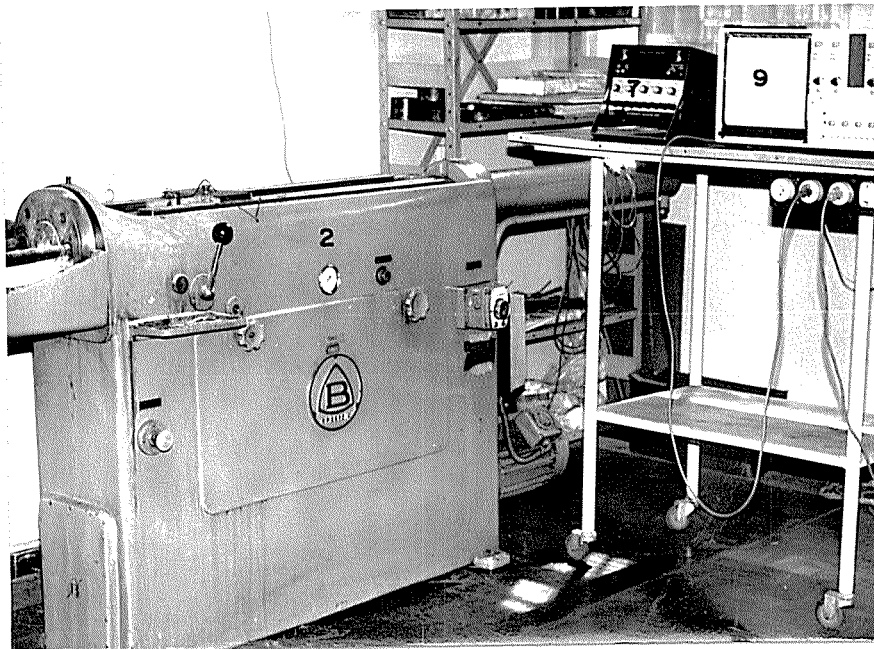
Banco de trefilação Bestlé-GT equipado.
